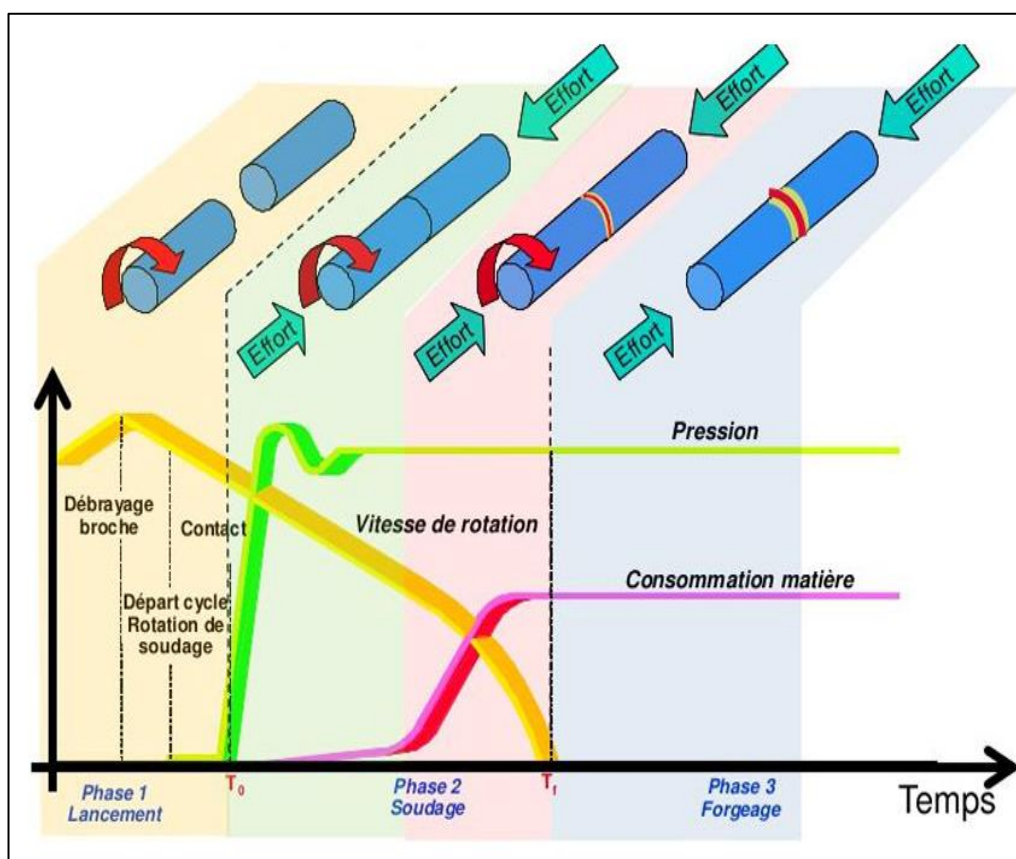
Le cycle de soudage par friction [7].
